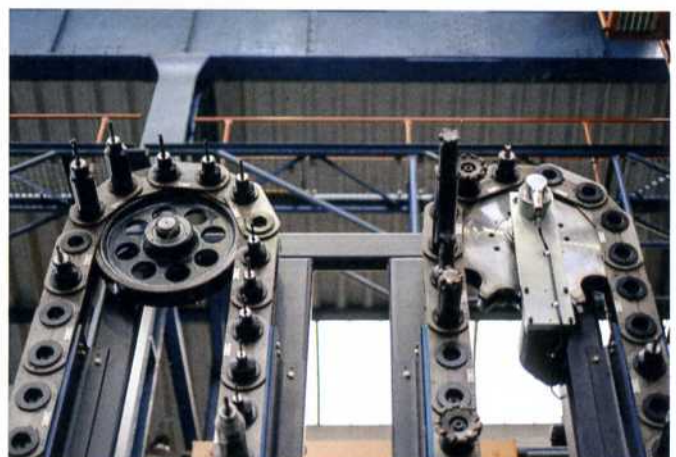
Das Werkzeugwechselsystem wurde erweitert und hat eine Kapazität bis zu 120 Werkzeugen.
